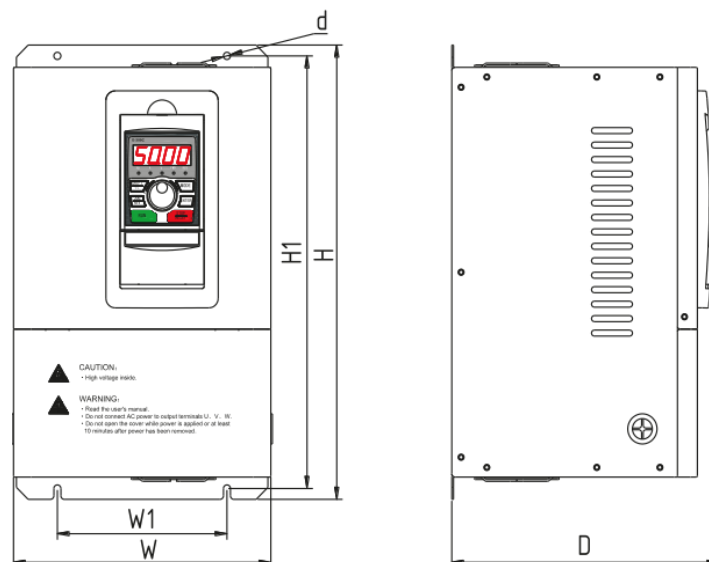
(Модель В) Внешний вид и размеры преобразователя частоты
